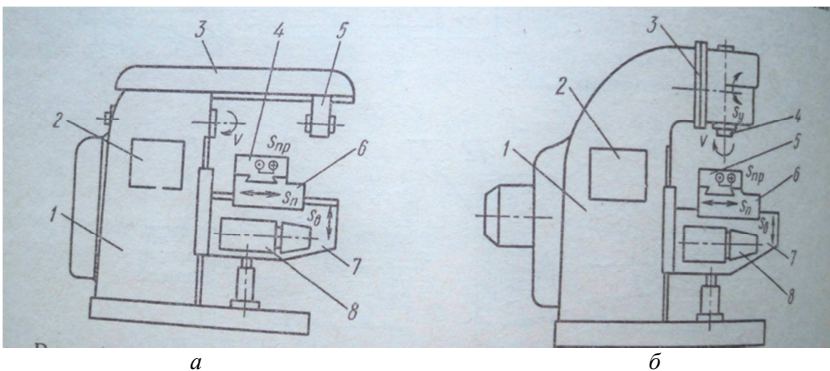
Горизонтально-фрезерний (а) та вертикально-фрезерний (б) верстати
